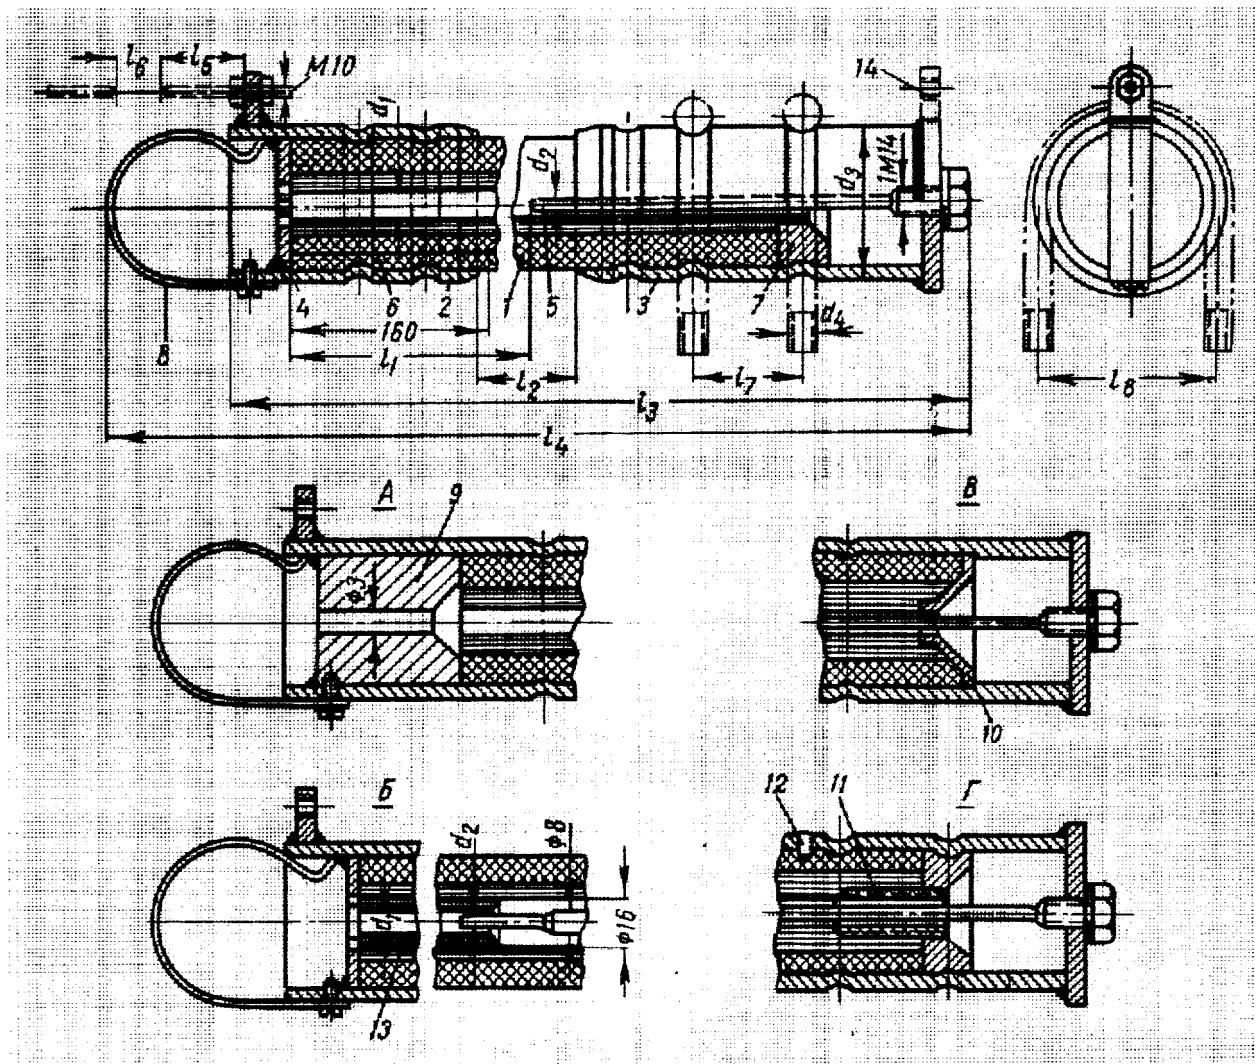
Конструкция разрядников: 1—фибробакелитовая трубка; 2—наконечник; 3—резервуар; 4—электрод открытого конца; 5—стержневой электрод; 6—дополнительный электрод (только для РТ-6-10); 7—конусная гайка; 8—указатель срабатывания; 9—заглушка; 10—воронка; 11—металлическая втулка; 12—штифт (для всех вариантов РТ-110); 13—фибровая вставка; 14—ушко (только для РТ-3); А—открытый конец РТ- $\frac{3}{0,2-1,5}$ ; Б—открытый конец РТ- $\frac{110}{0,4-2,2}$  (вариант I и II); В—закрытый конец РТ-3 и РТ- $\frac{35}{0,4-3}$ ; Г—закрытый конец всех РТ-110 (кроме РТ- $\frac{110}{2-10}$ ).
